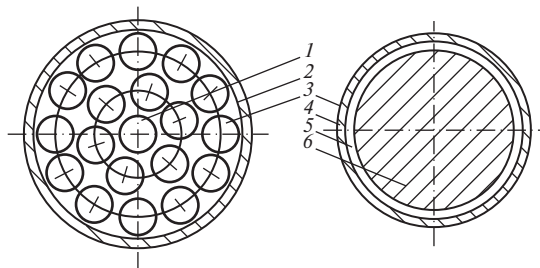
Схематический разрез канала и твэла реактора РБМК:
